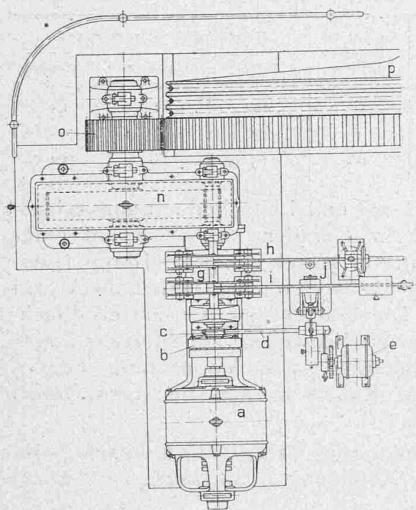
Ansichten und Grundriss des Triebwerks. Maßstab 1:50.
